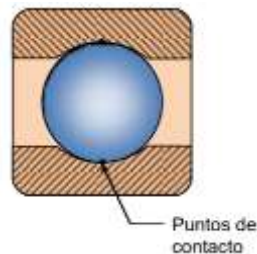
Punto de contacto de esfera; Fuente: Elementos de Máquinas
